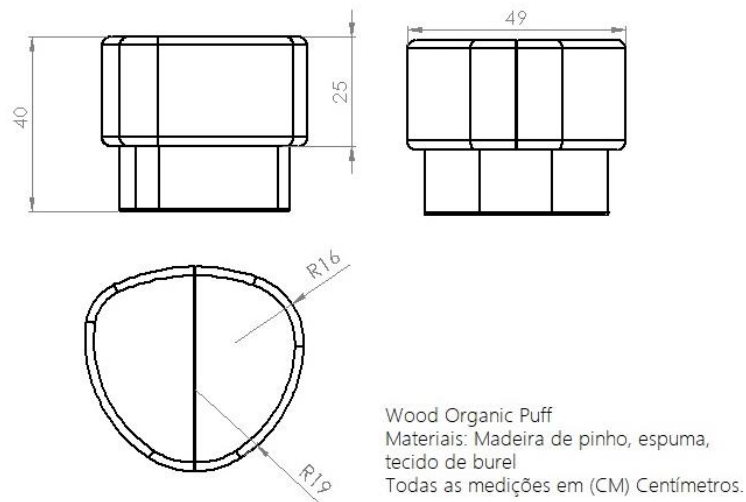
Desenho técnico CAD 3D *Wood Organic
